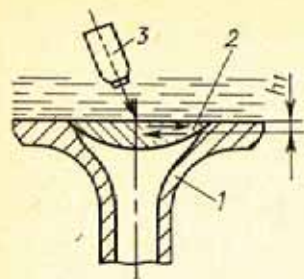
Контроль сварного шва клапана поверхностными волнами
